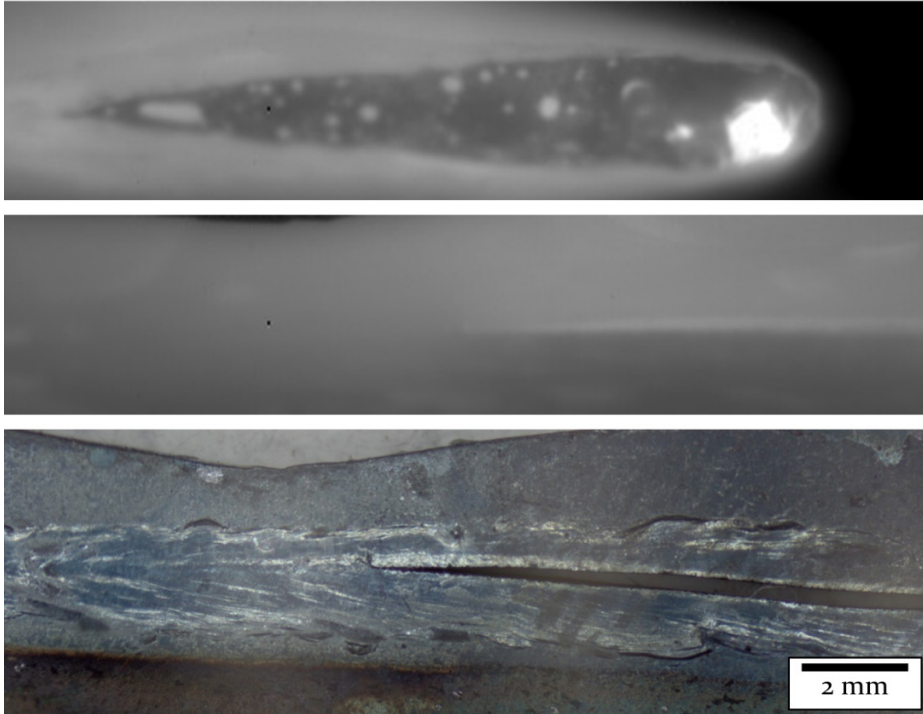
Oben: Einzelbild einer exemplarischen Schmelzbadgeometrie aus einer Thermografieaufnahme, Mitte: Einzelbild des im Schweißprozess entstandenen Nahtmittenrisses, Unten: Aufsicht der Schweißnaht mit Nahtmittenriss; $P = 3,50 \text{ kW}$; $v_L = 35 \text{ mm/s}$; $E = 100 \text{ J/mm}$; $d_F = 170 \text{ }\mu\text{m}$
